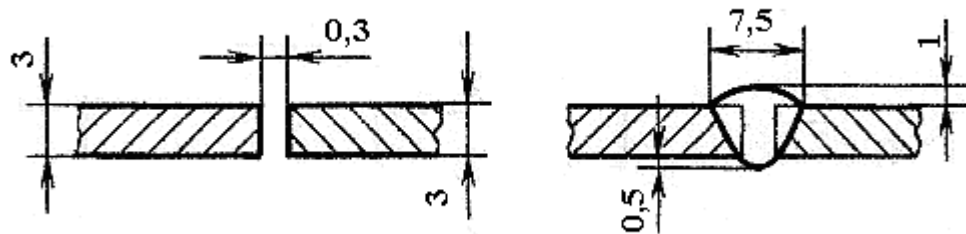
Зварне з'єднання С2 ГОСТ 14771-76
